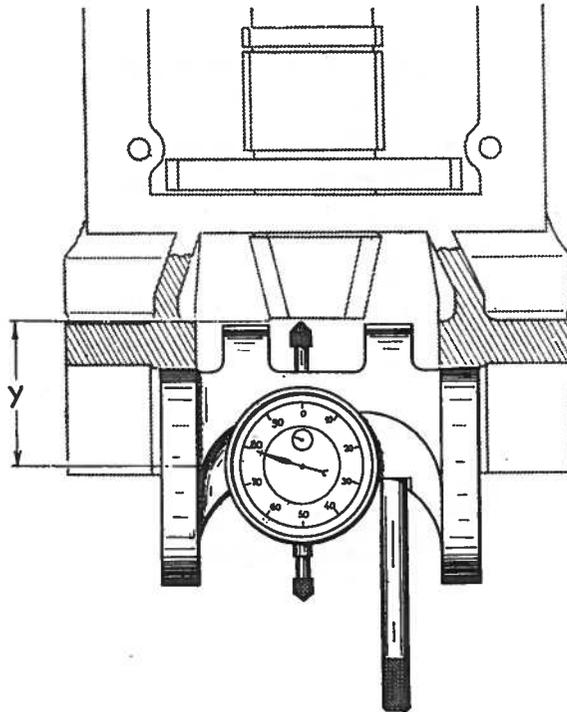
RÉGLAGE DU JEU D'ENGRÈNEMENT
